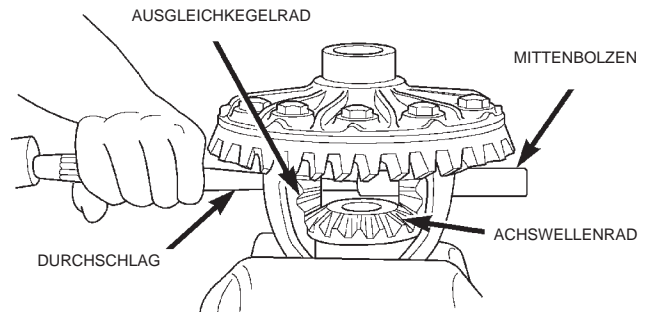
Haltewerkzeug für Ausgleichkorb
